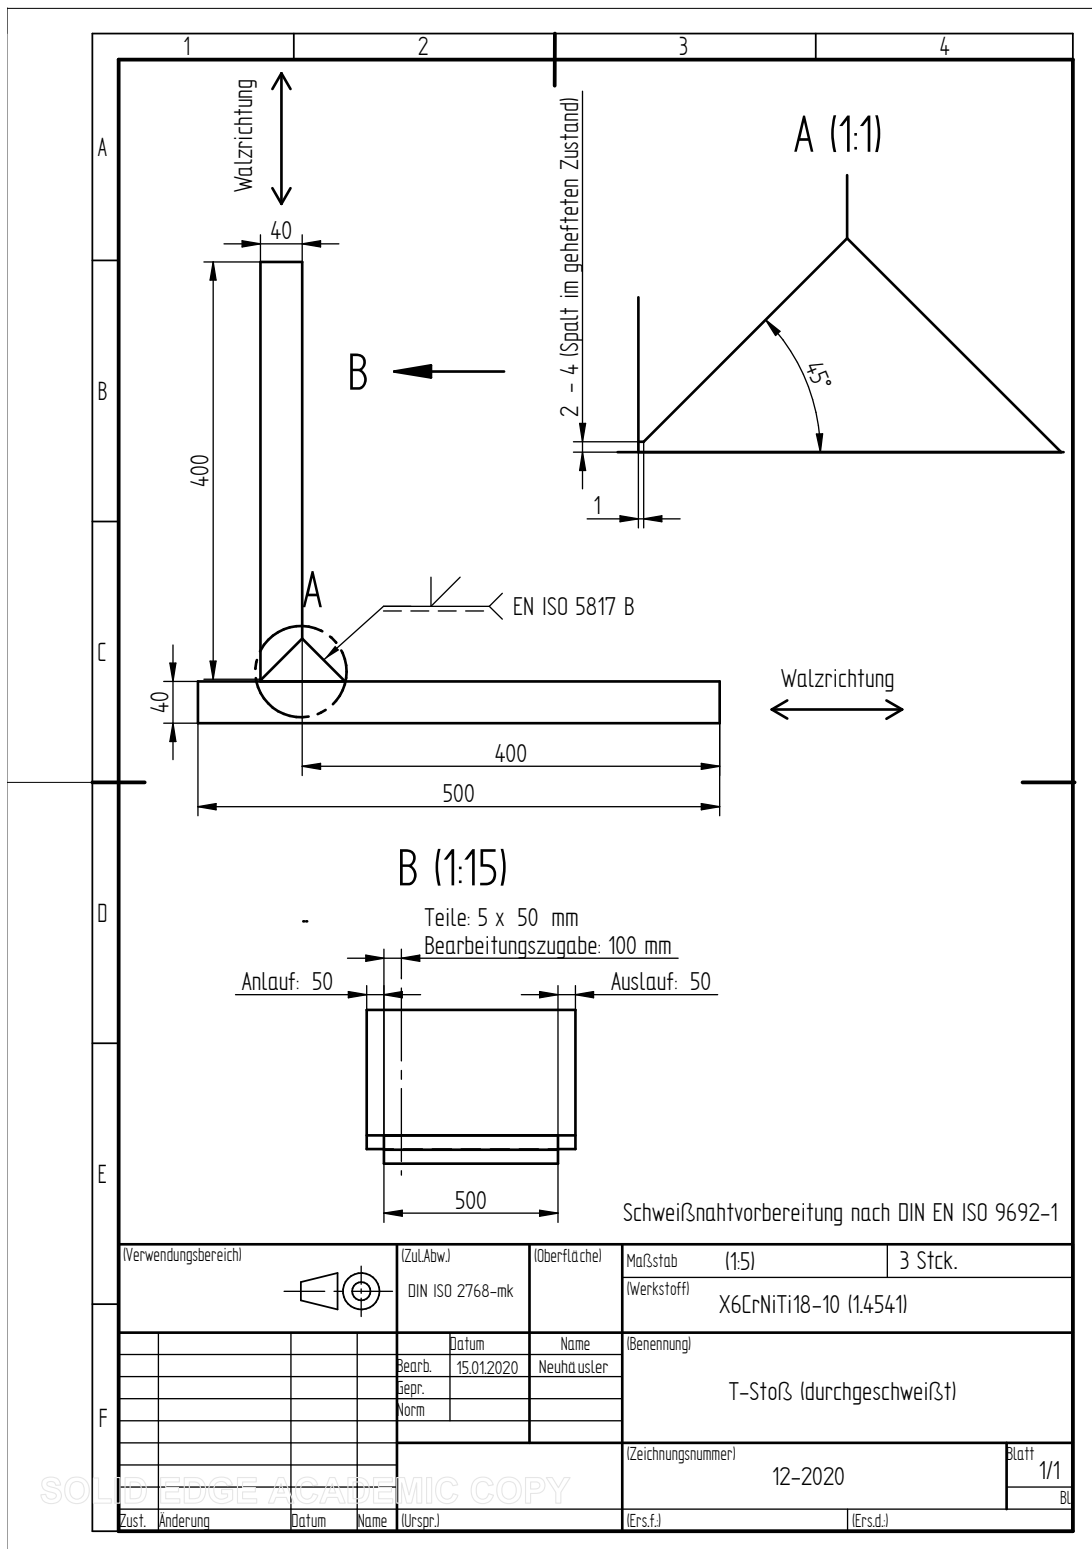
Fertigungszeichnung für die T-Stoß Proben aus 1.4541 [67].
